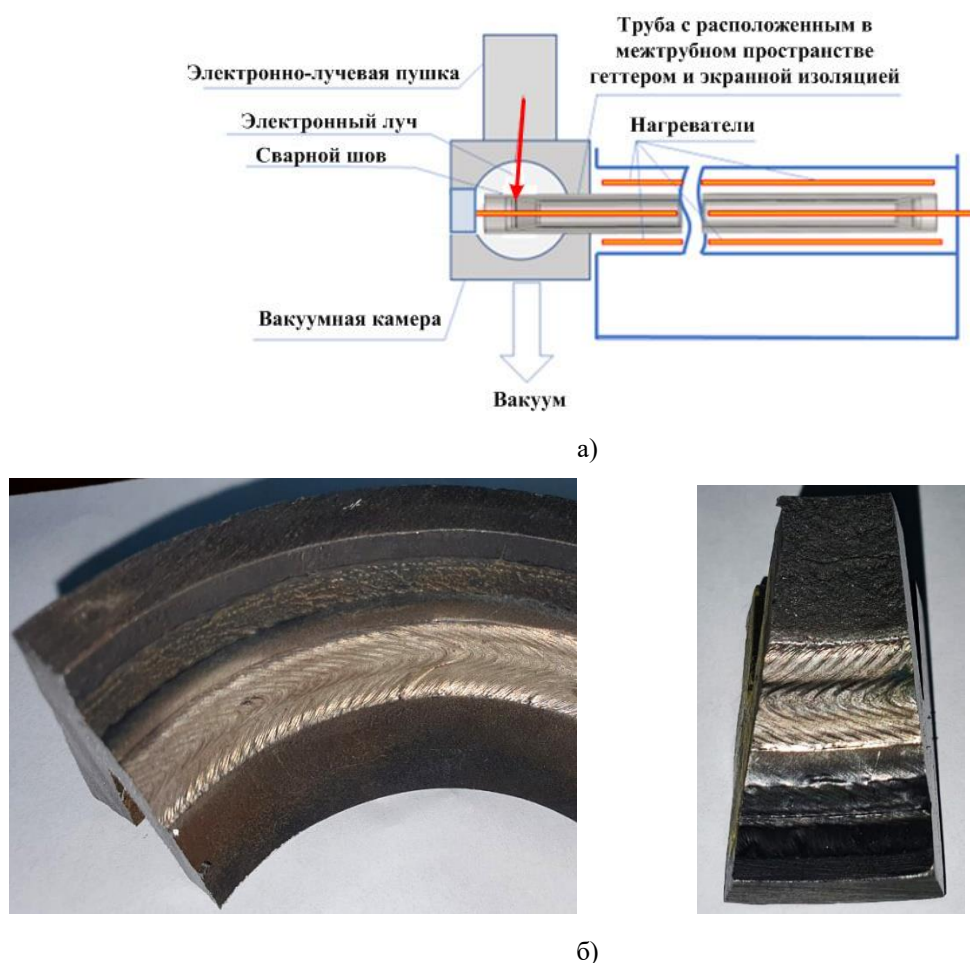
Схема установки (а) и внешний вид сварного соединения (б).
